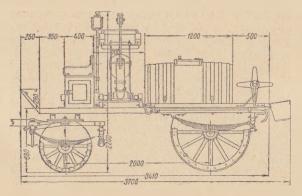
Насосно-бочечный рессорный пароконный ход.
